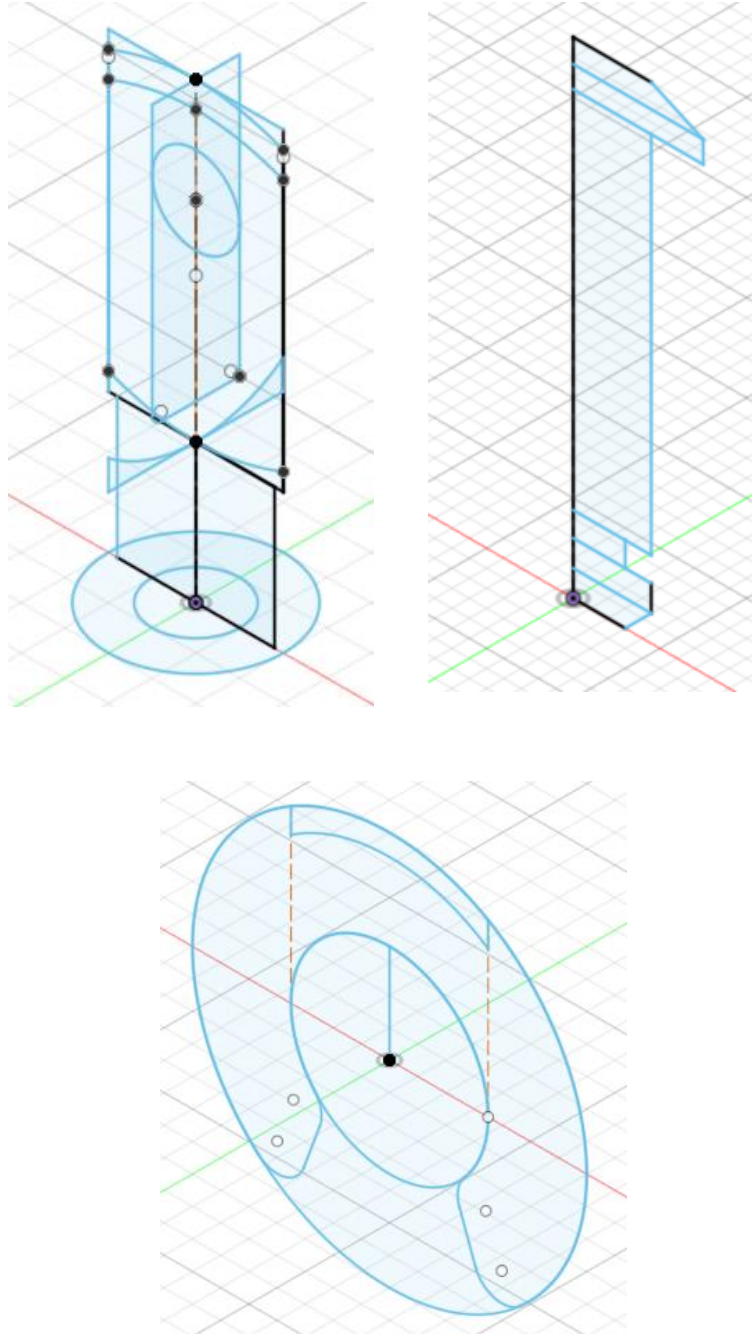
To Drawing του Pillow Block Bearing with Spherical Ball.
